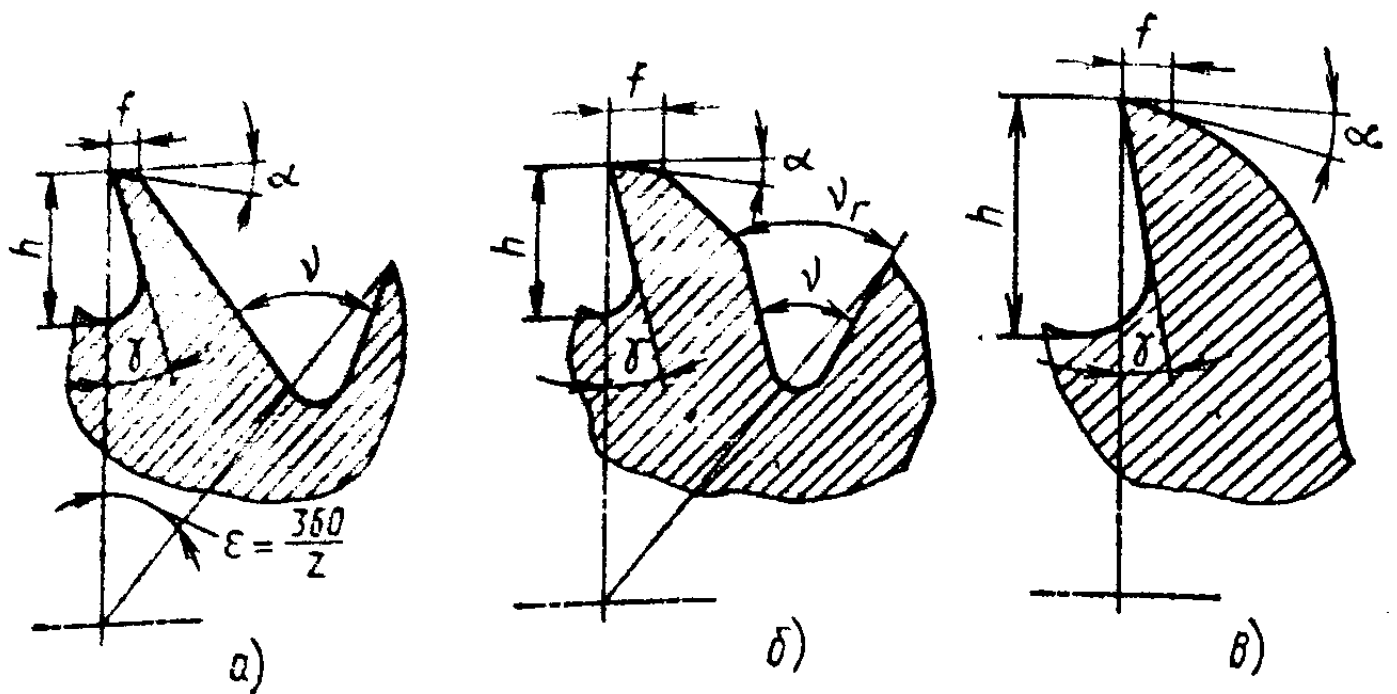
Конструктивные и геометрические параметры зубьев фрезы
